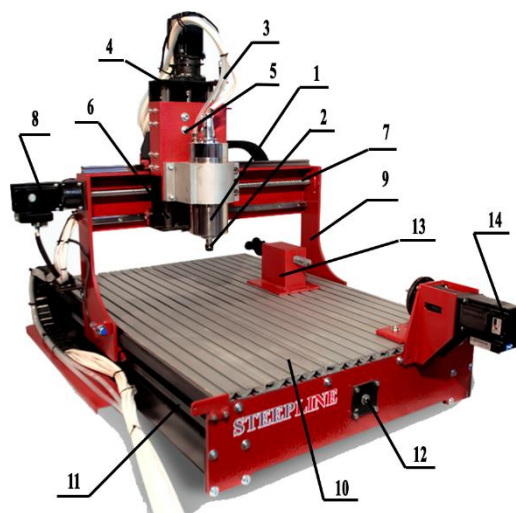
Станок для гравірувально-фрезерних робіт SL01Б
